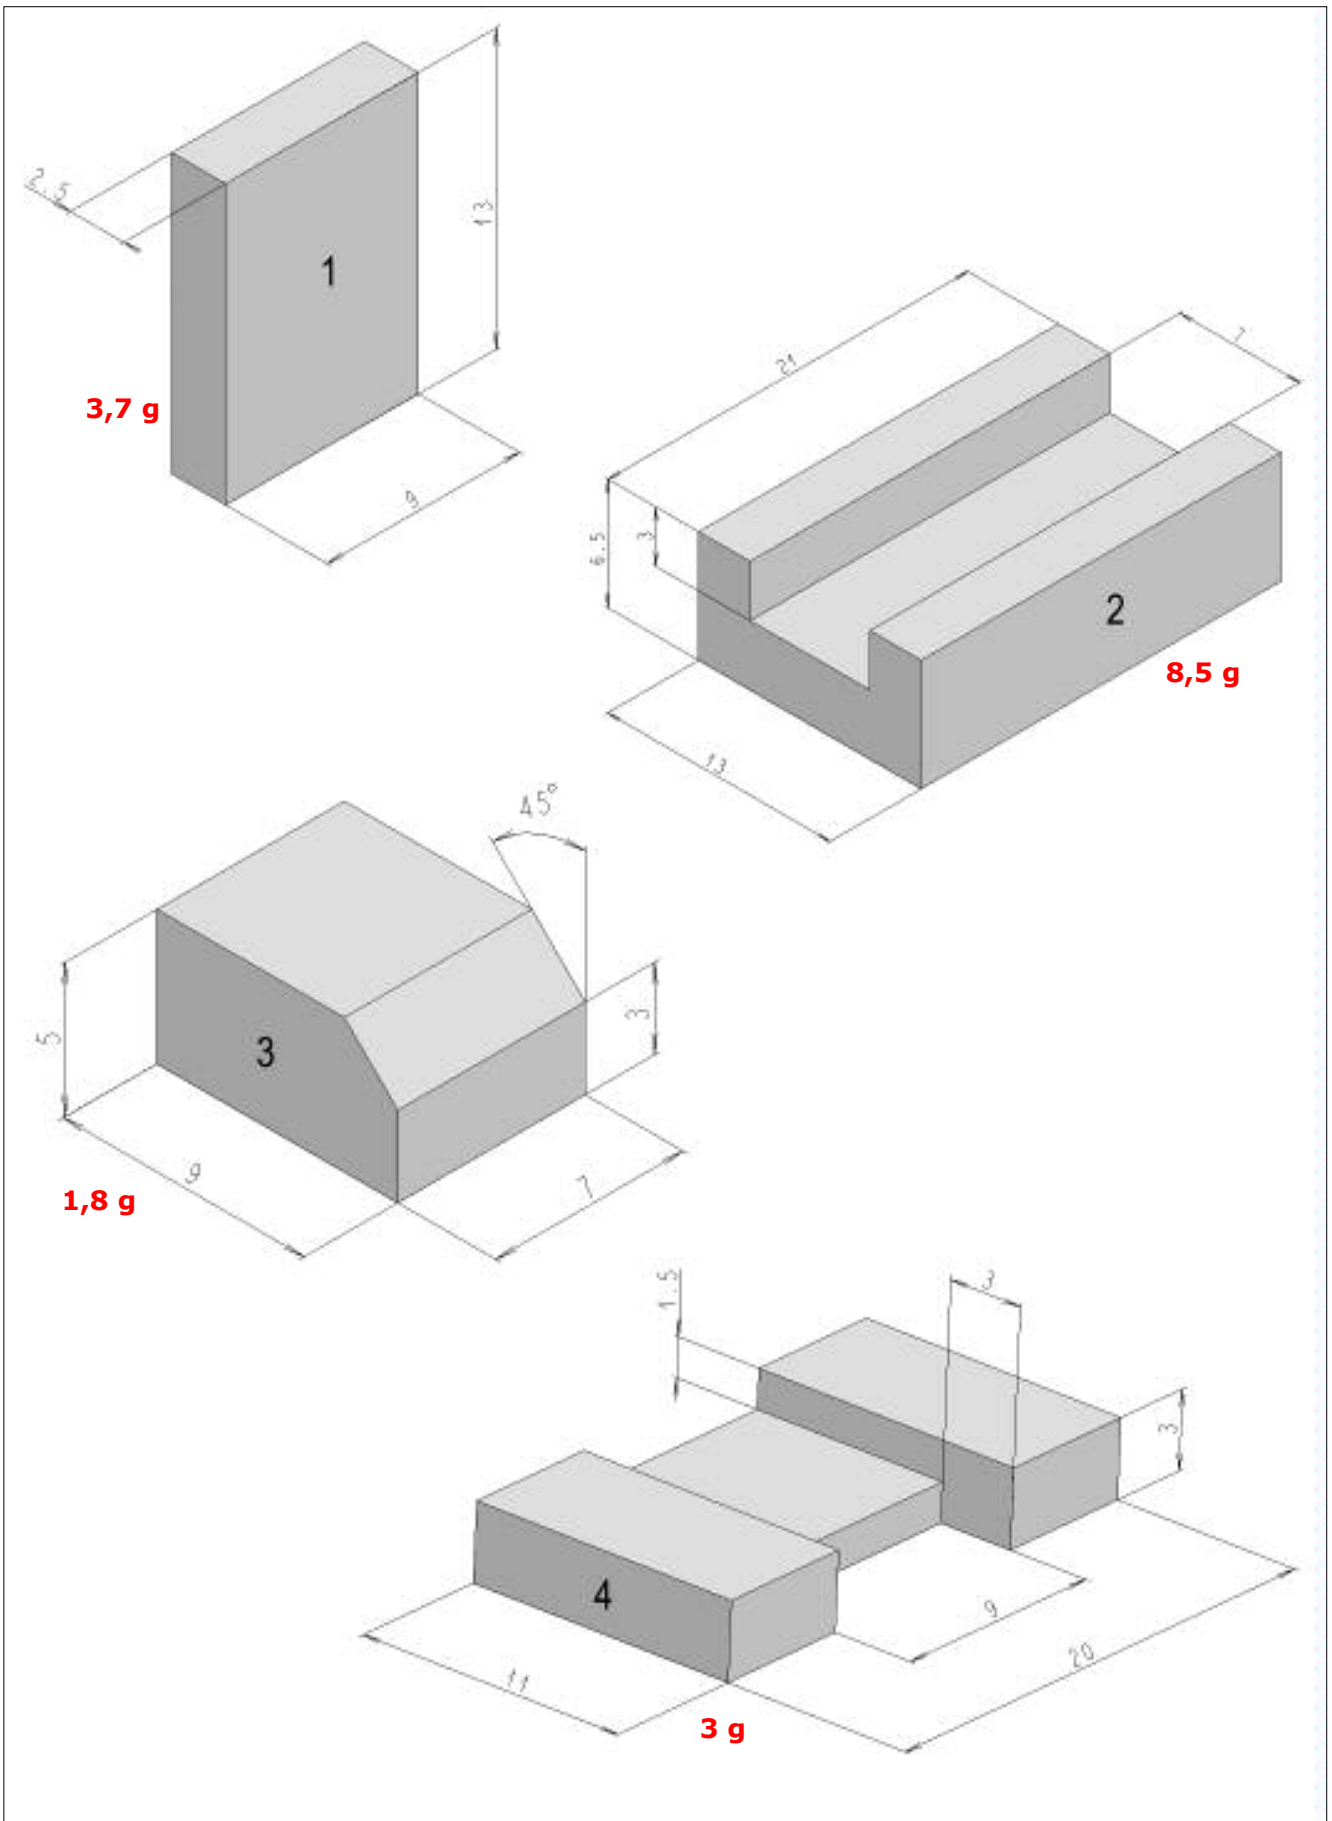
Detail vrchního závaží s vyfrézovanou drážkou
